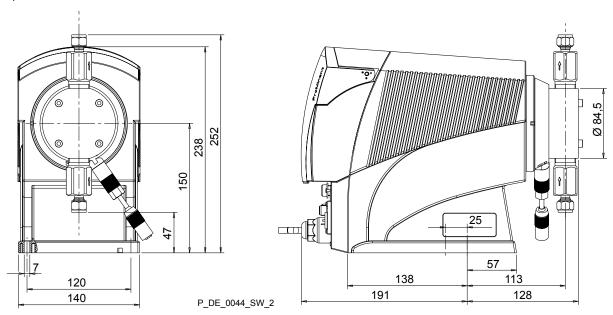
Hoja de dimensiones del tipo delta® 1612 - 0730, versión de material SS; dimensiones en mm
